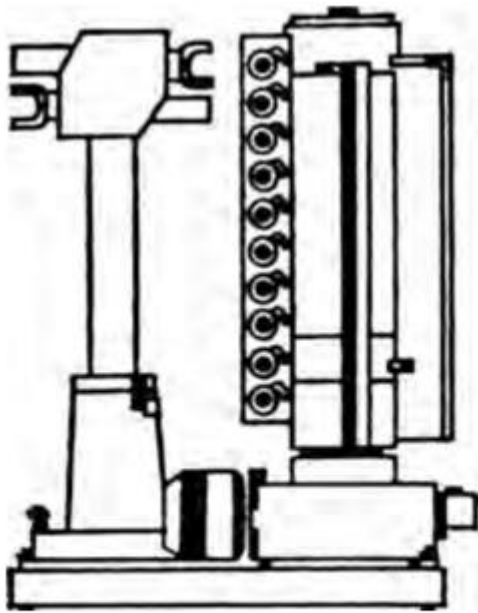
Напольный передвижной автооператор для смены инструмента при индивидуальном или групповом обслуживании металлорежущих станков
